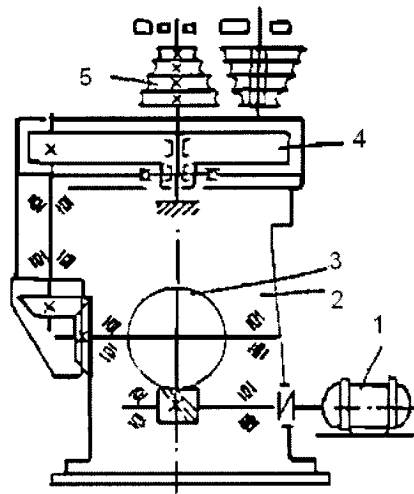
Схема трубозгинального механізму ВМС-23: 1 — електродвигун; 2 — станина; 3 — черв'ячний редуктор; 4 — робочий механізм; 5 — ролики
